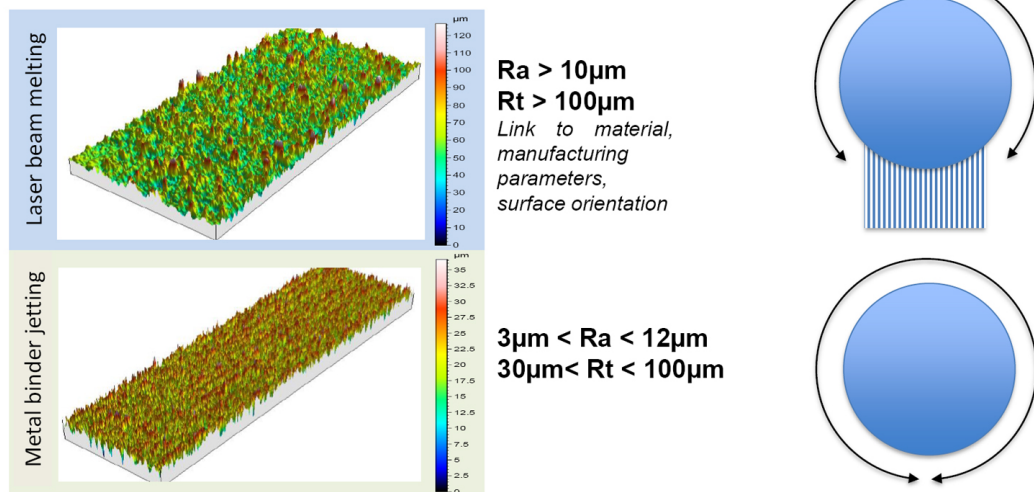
Scan de surface et mesure des rugosités surfaciques sur des éléments imprimés en technique Laser Beam Melting et Metal Binder Jetting (machine de métrologie optique 3D de surface de haute résolution). On constate la rugosité majorée dans le cas de bagues imprimées par Laser Beam Melting.
